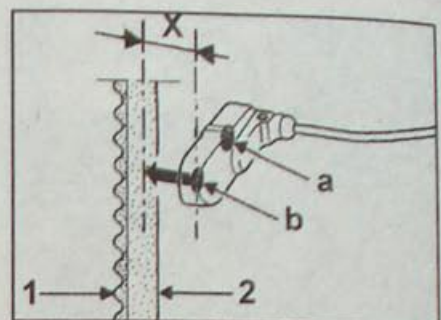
Измерение натяжения ремня привода газораспределительного механизма с использованием датчика (b) считывающей головки:
